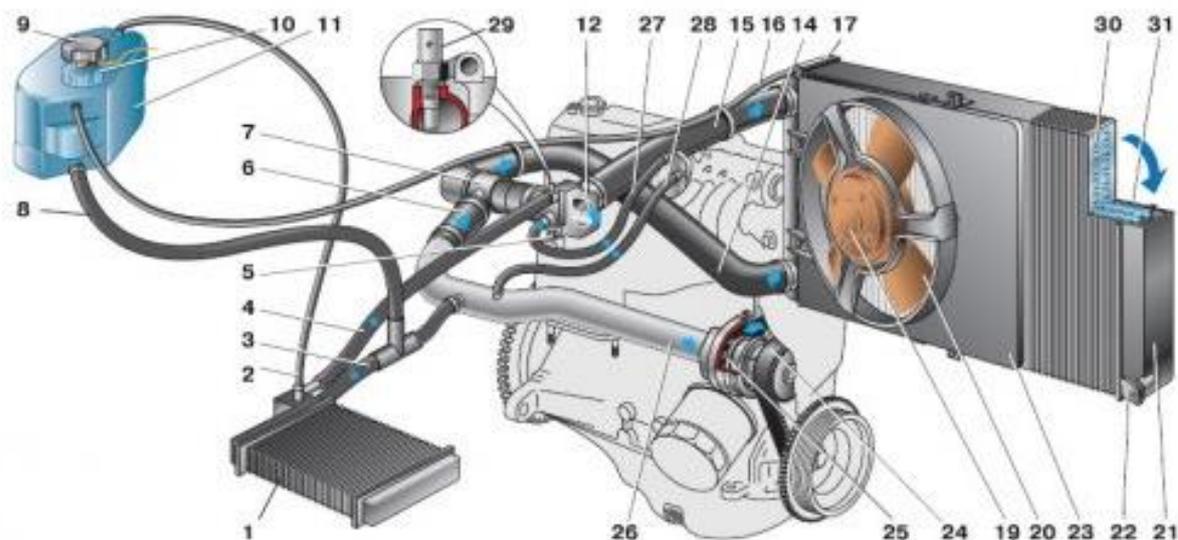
Схема охлаждения двигателя ВАЗ-2110 (с инжектором):
